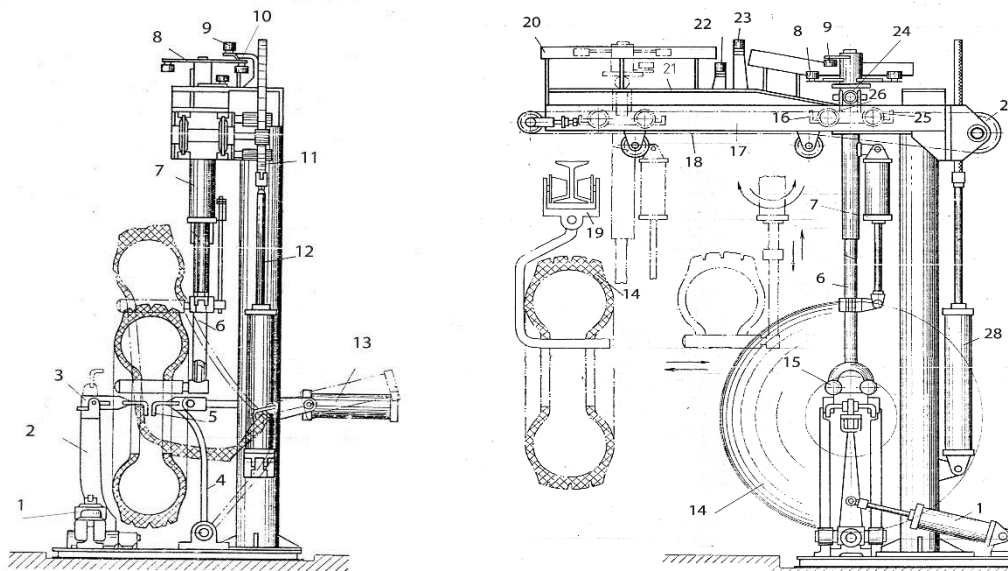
Устройство для осмотра и ремонта покрышек: 1,7,13,28-пневмоцилиндры; 2,4-рычаги; 3,5-захваты; 6-телескопическая штанга; 8,10-дугообразные плечи крестообразного рычага; 9-ролики крестообразного рычага; 11-рейка; 12-шток пневмоцилиндра; 13-стойка; 14-покрышка; 15,25,26- опорные ролики 16-подвижная каретка; 17-направляющая; 18-цепная передача; 19-опора качения; 20-опоры роликов; 21-наклонная направляющая; 22,23-упоры; 24-подпружиненные ролики; 27-приводная звёздочка.
